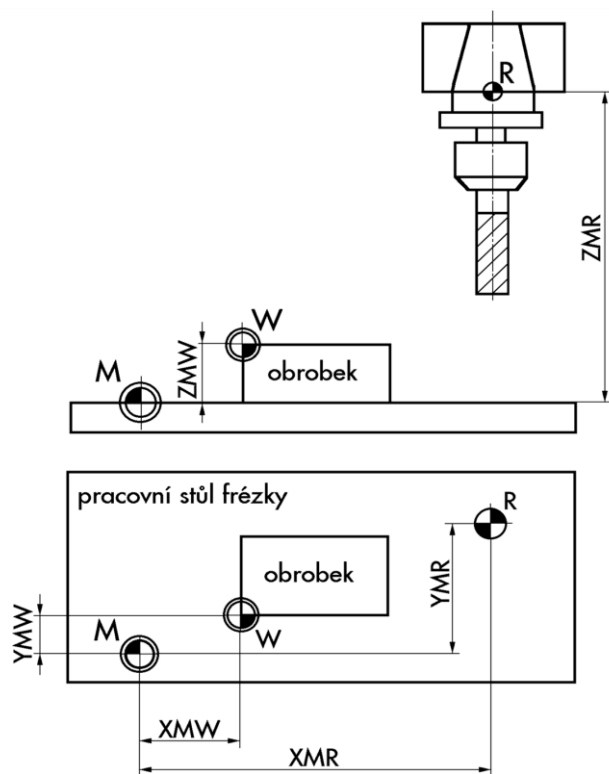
Symboly a značení vztažných bodů NC/ CNC obráběcího stroje
